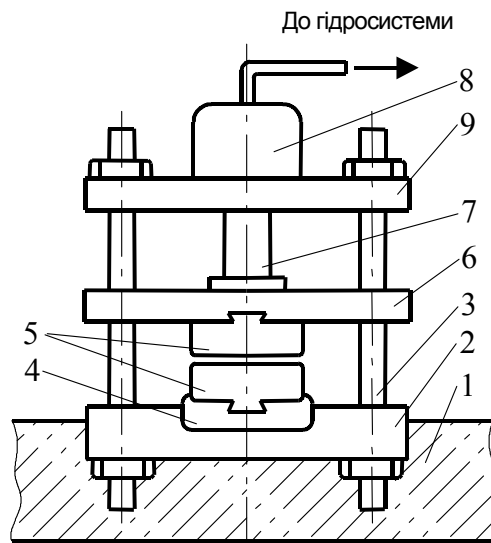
Загальний вигляд гідравлічного преса: 1 – фундамент; 2 – нижня нерухома плита; 3 – колони; 4 – штампотримач; 5 – бойки; 6 – верхня рухома плита; 7 – шток-поршень; 8 – гідроциліндр; 9 – верхня нерухома плита
